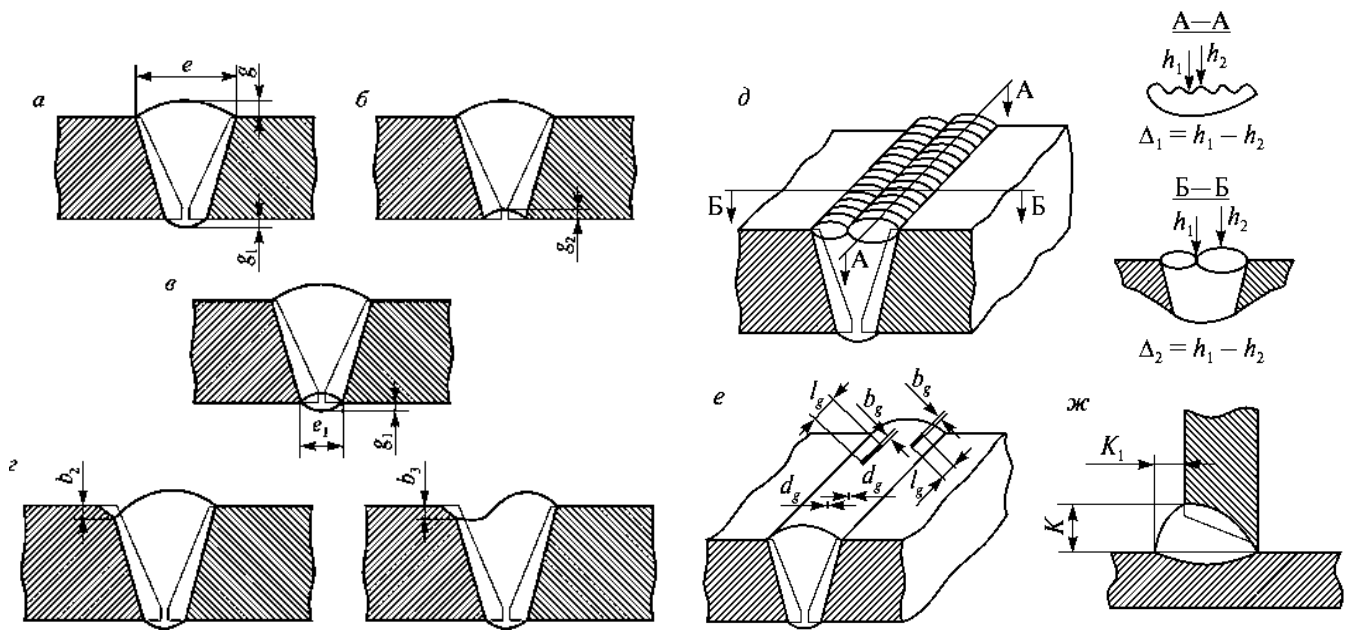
Конструктивные элементы и дефекты сварного шва, подлежащие измерительному контролю:
